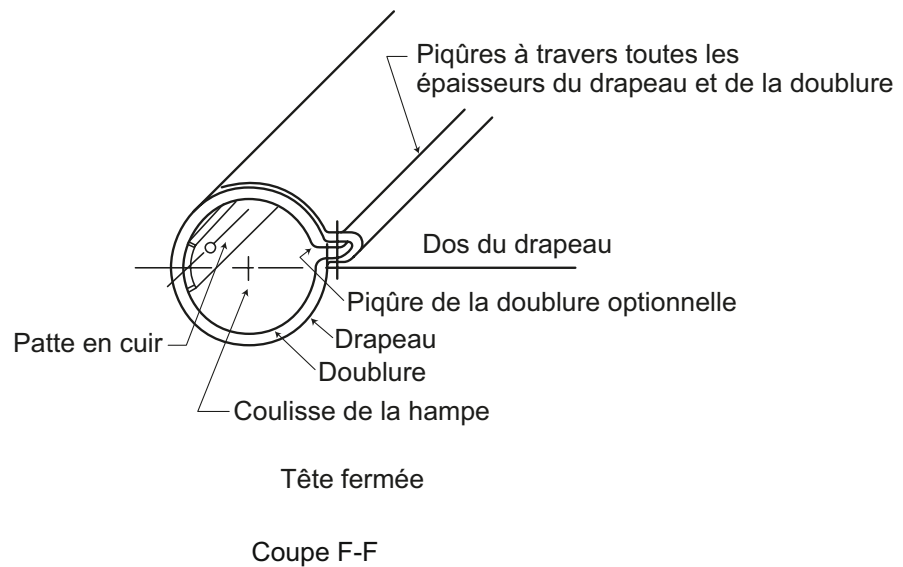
Détails de fabrication — Drapeau de sous-type 3B
